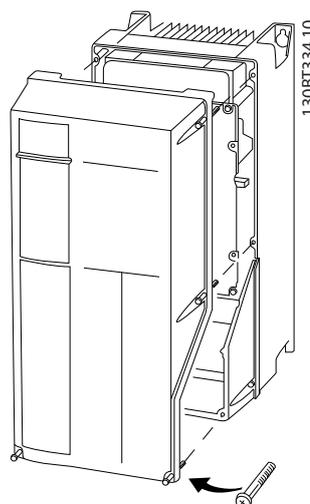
Accès au câblage des protections IP55 et IP66
